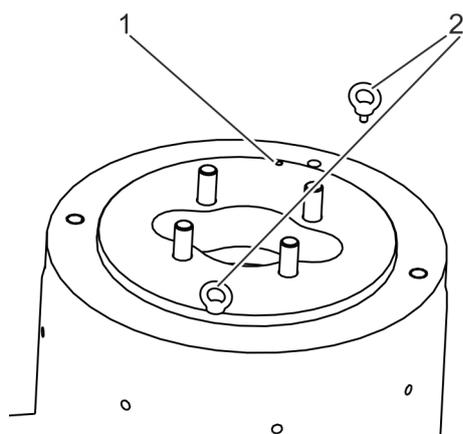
Vissage des anneaux de levage dans le couvercle de serrage
